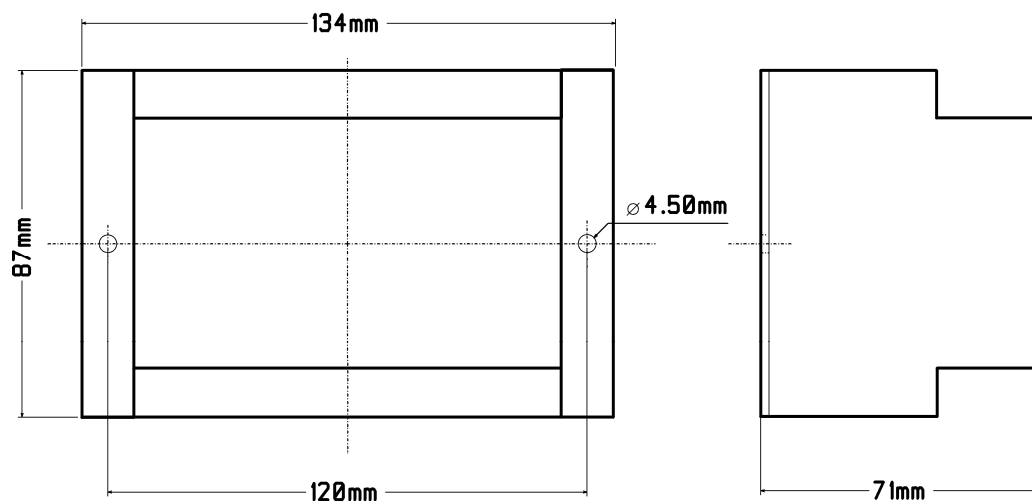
Габаритные и присоединительные размеры преобразователей OLD/ML
